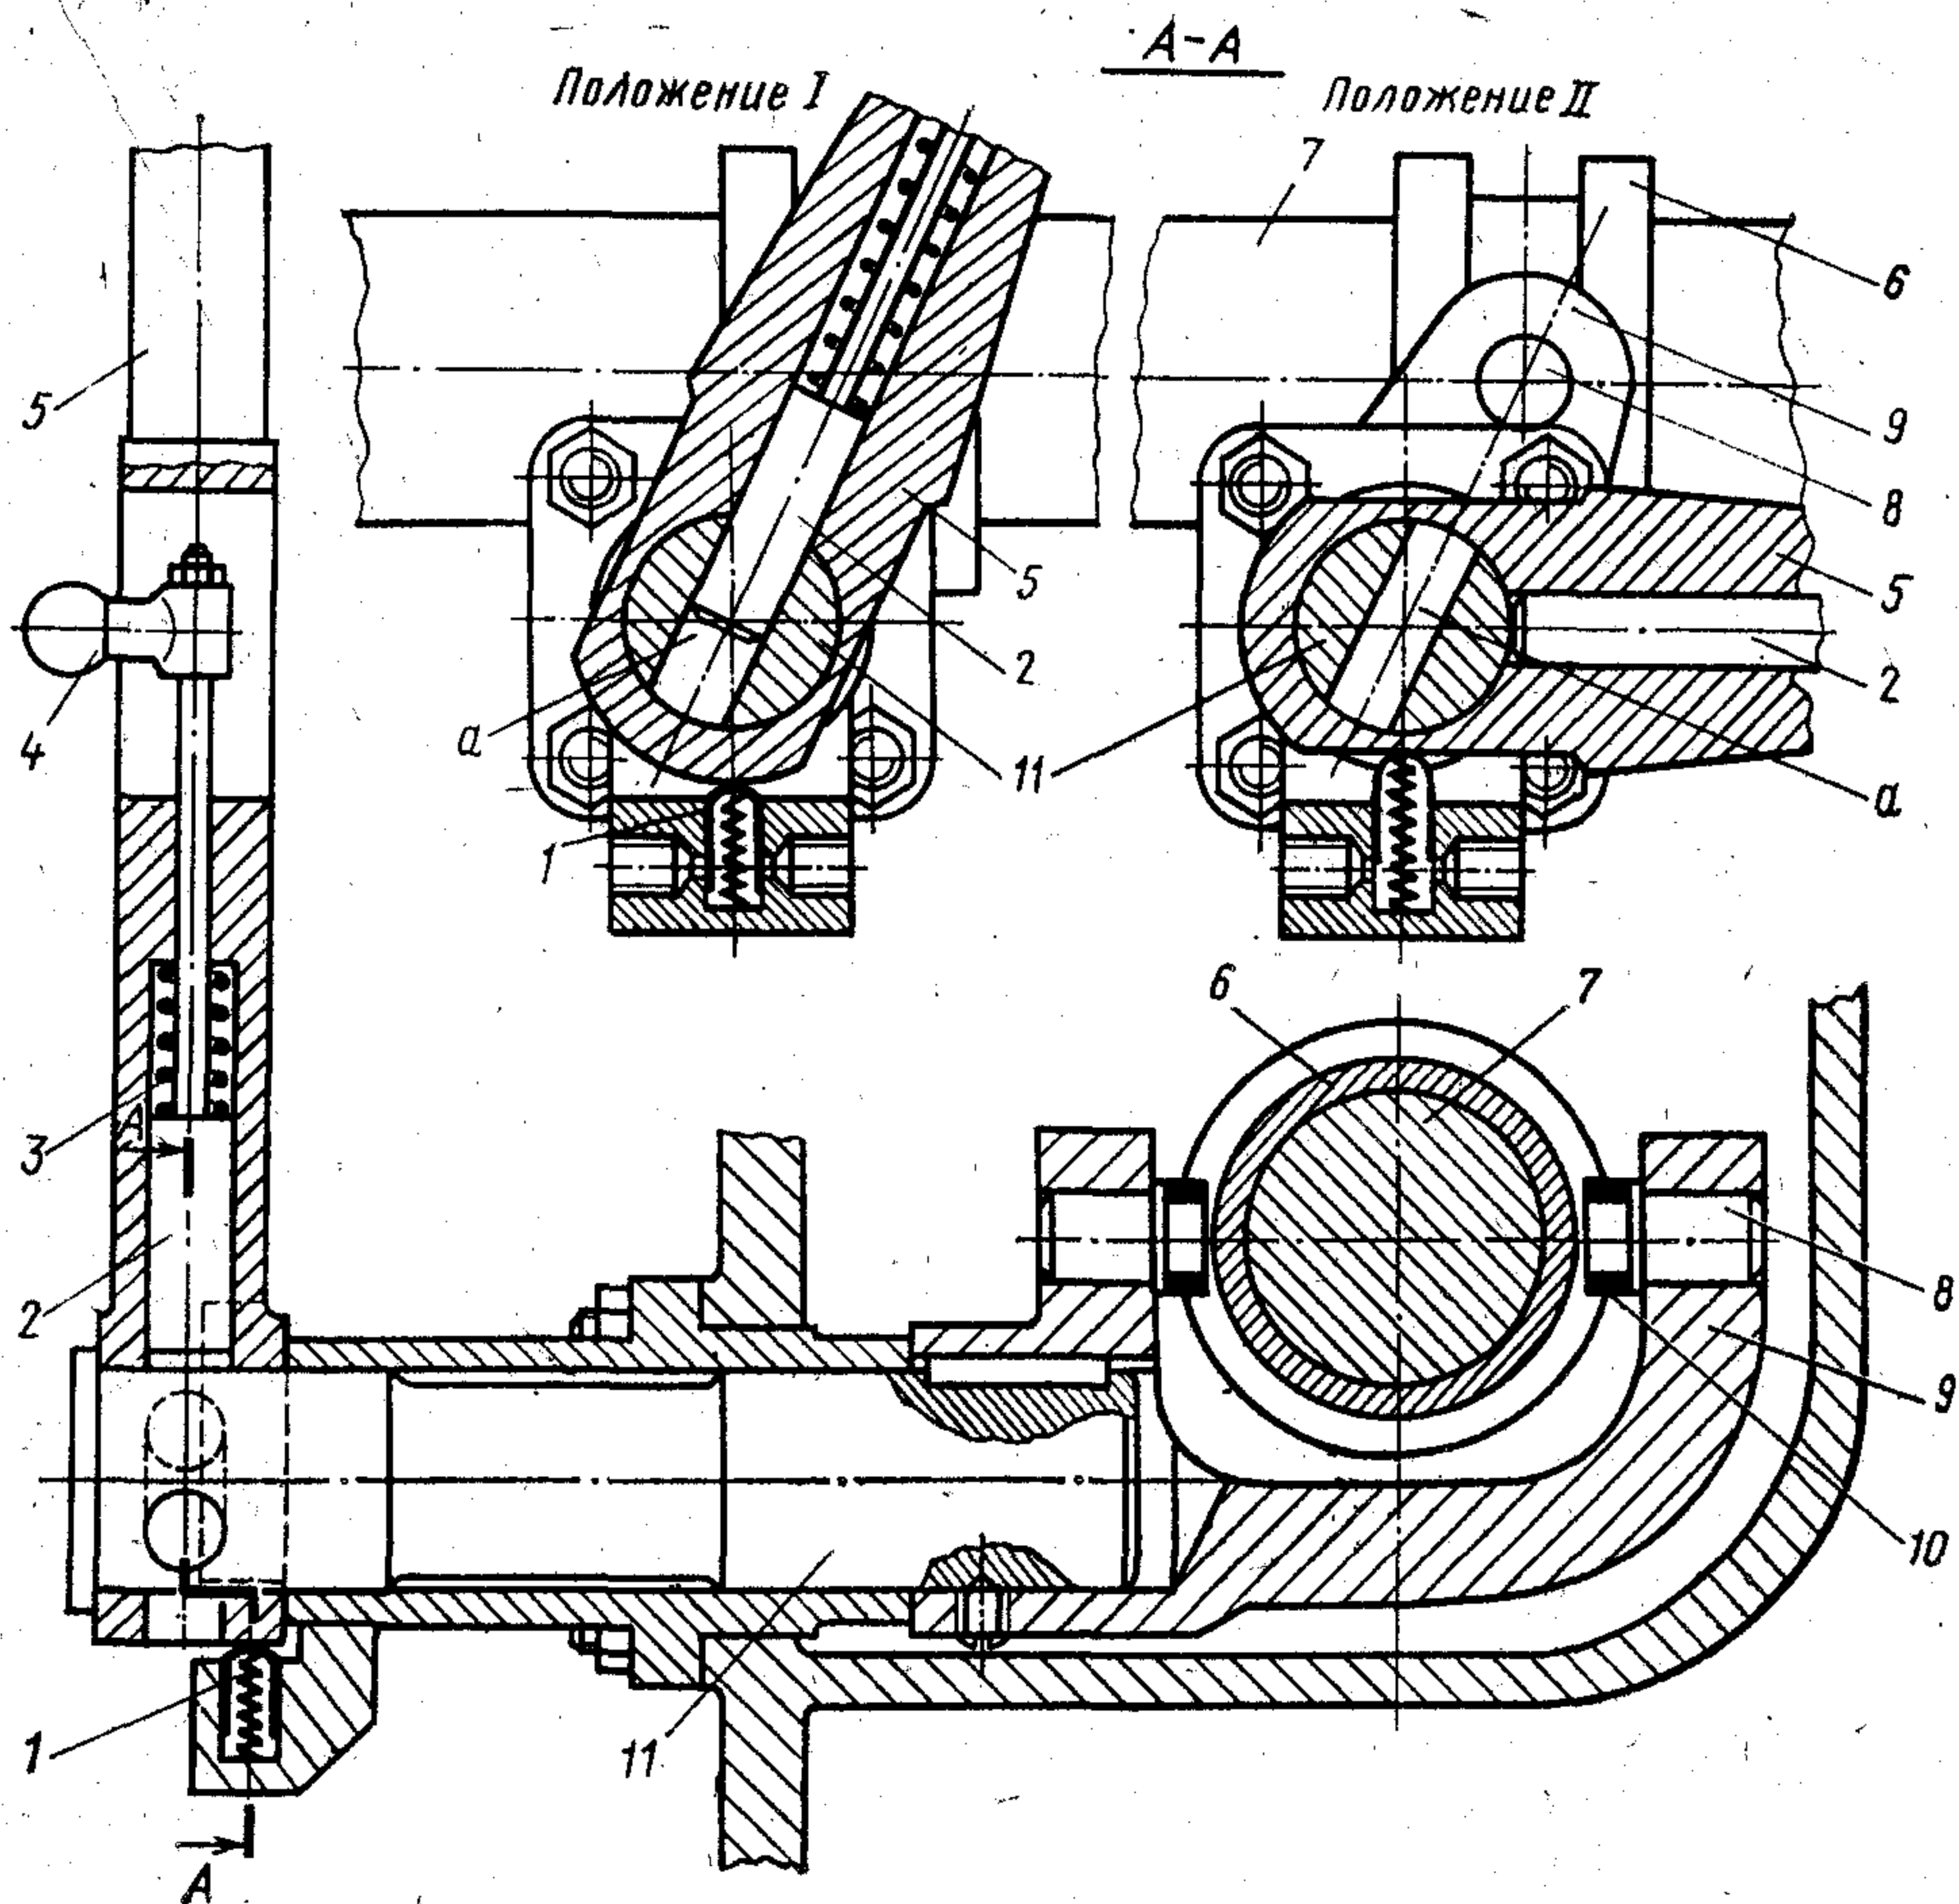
Механизм ручного реверсирования двигателя 6Л275Рр/II
